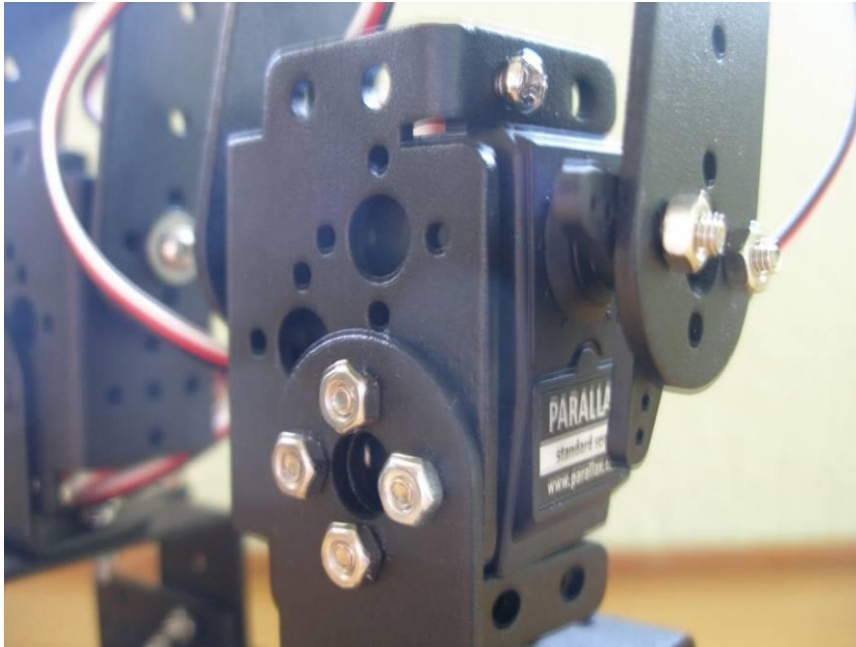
Instalación del servomotor para la rodilla izquierda del robot
